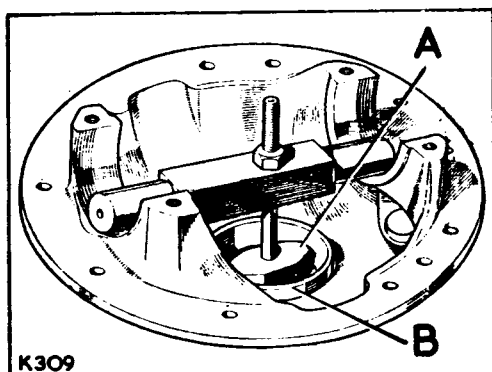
Desmontaje a presión de la pista exterior de rodamiento.
